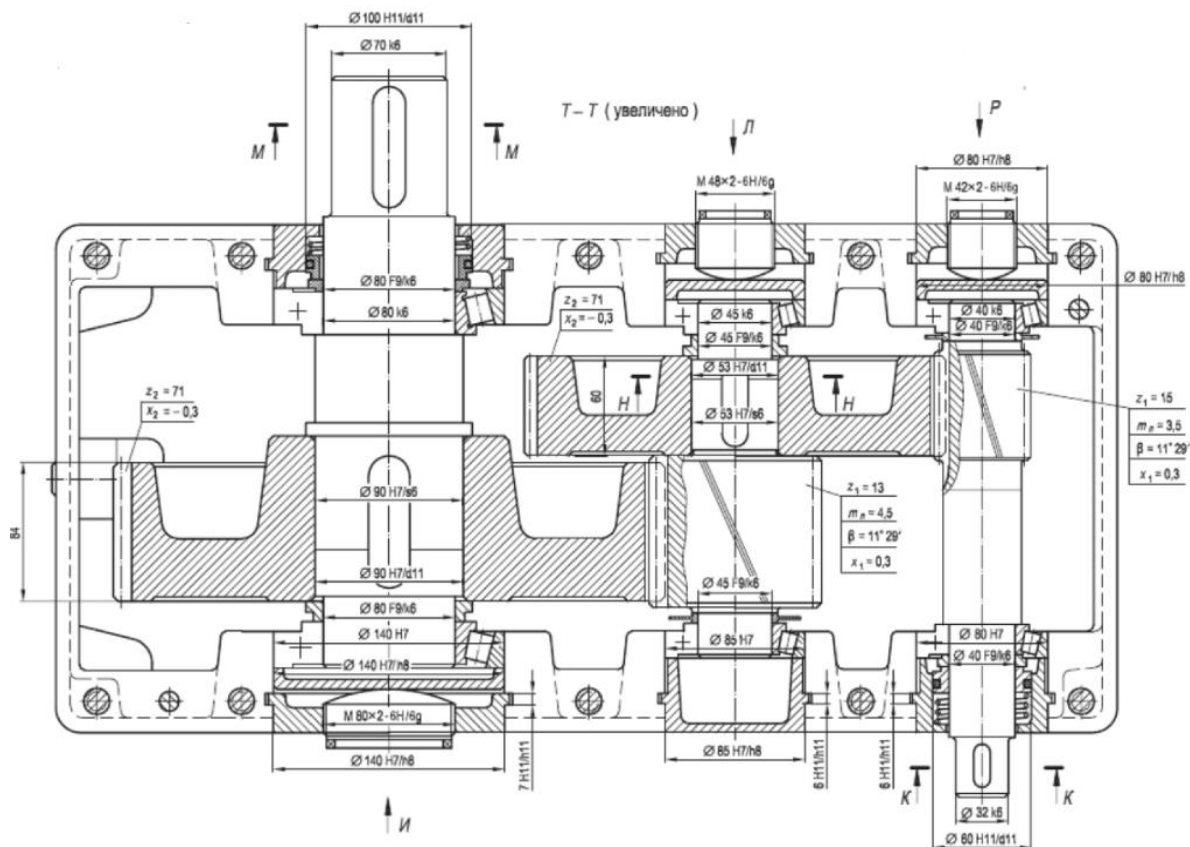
Двухступенчатый цилиндрический редуктор с коническими подшипниками
